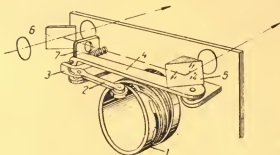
Схема механизма дальномера фотоаппаратов ФЭД и Зоркий
